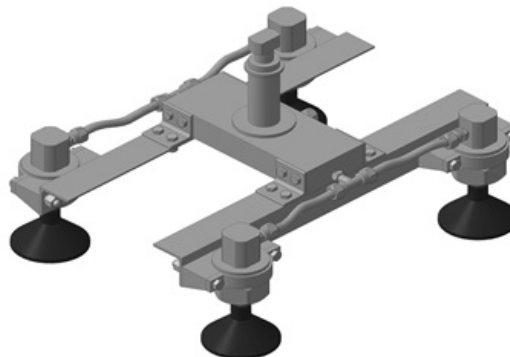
Вакуумний хватний пристрій для листових заготовок
